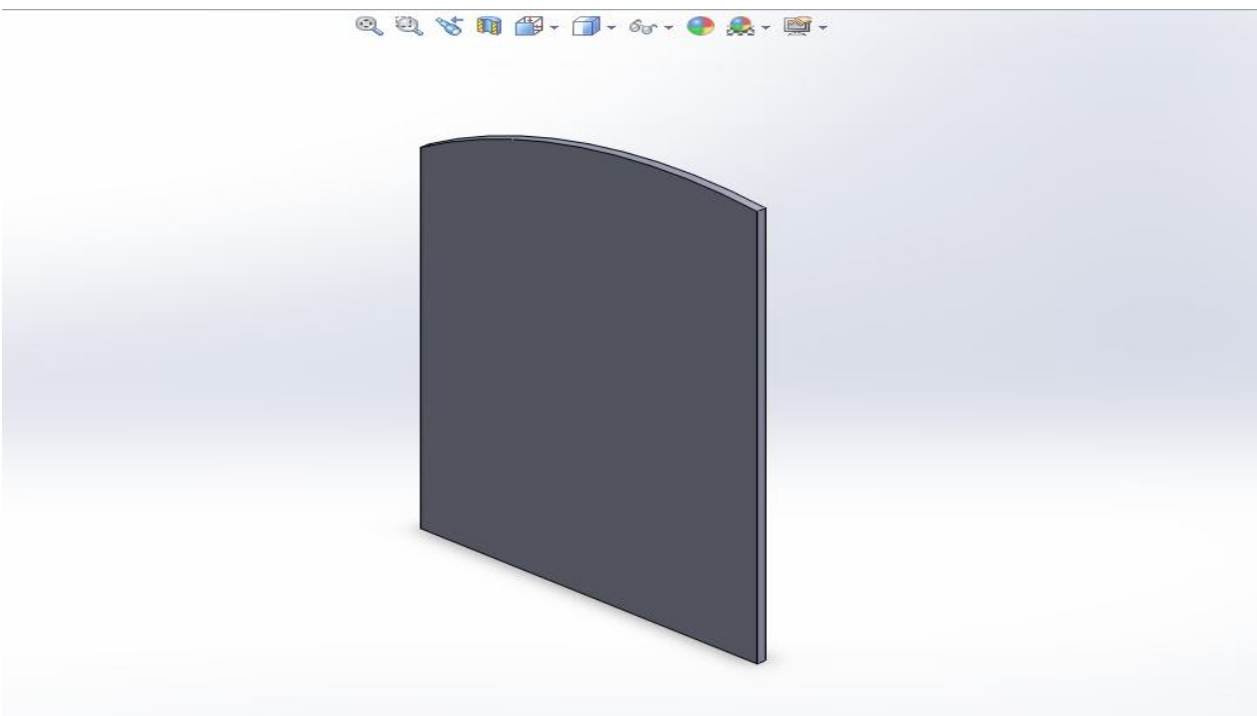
Δημιουργία λοξοτόμησης με την εντόλη CHAMFER
